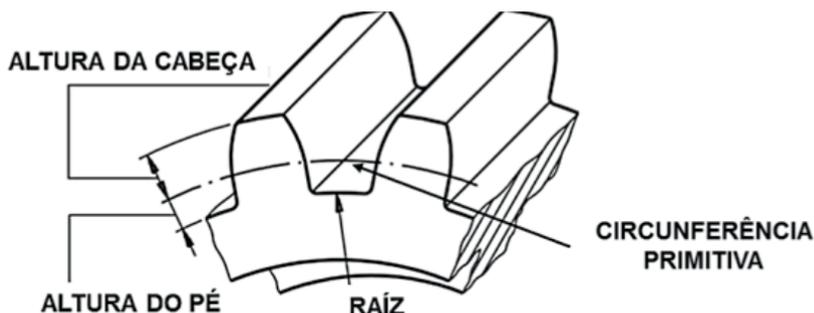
| Partes de uma engrenagem e tipos de corpo
